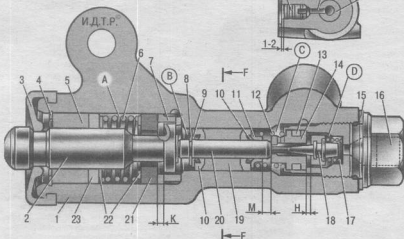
Регулятор давления: 1 — корпус регулятора давления; 2 — поршень; 3 — защитный колпачок; 4, 8 — стопорные кольца; 5 — втулка поршня; 6 — пружина поршня; 7 — втулка корпуса; 9, 22 — опорные шайбы; 10 — уплотнительные кольца толкателя; 11 — опорная тарелка; 12 — пружина втулки толкателя; 13 — кольцо уплотнительного седла клапана; 14 — седло клапана; 15 — уплотнительная прокладка; 16 — пробка; 17 — пружина клапана; 18 — клапан; 19 — втулка толкателя; 20 — толкатель; 21 — уплотнитель головки поршня; 23 — уплотнитель штока поршня; 24 — заглушка; А, Д — камеры, соединенные с главным цилиндром; В, С — камеры, соединенные с колесными цилиндрами задних тормозов; К, М, Н — зазоры
